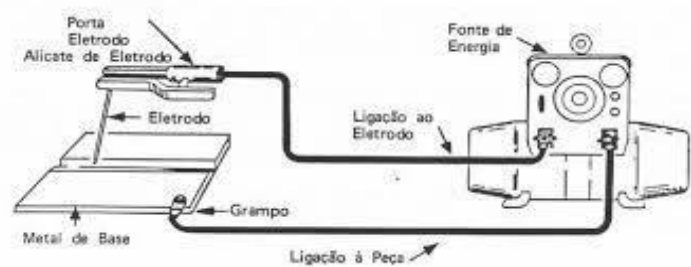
Circuito de soldagem para o processo com eletrodos revestidos.
